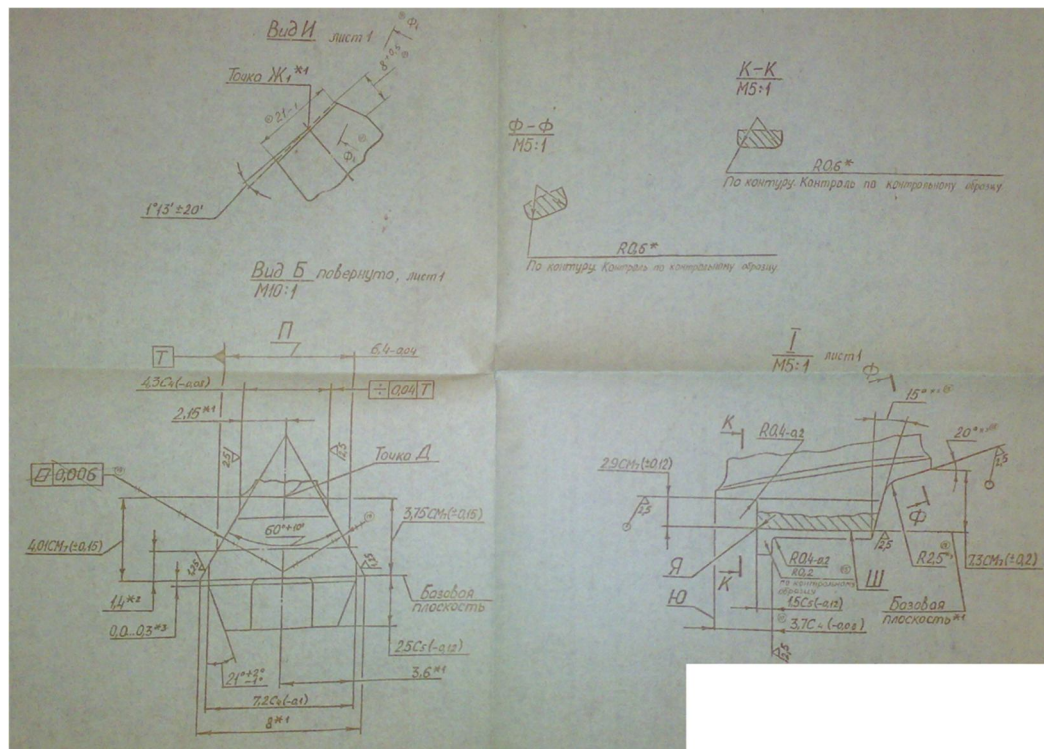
Фото кресления лопатки компрессора ТРД (Лист 1)
